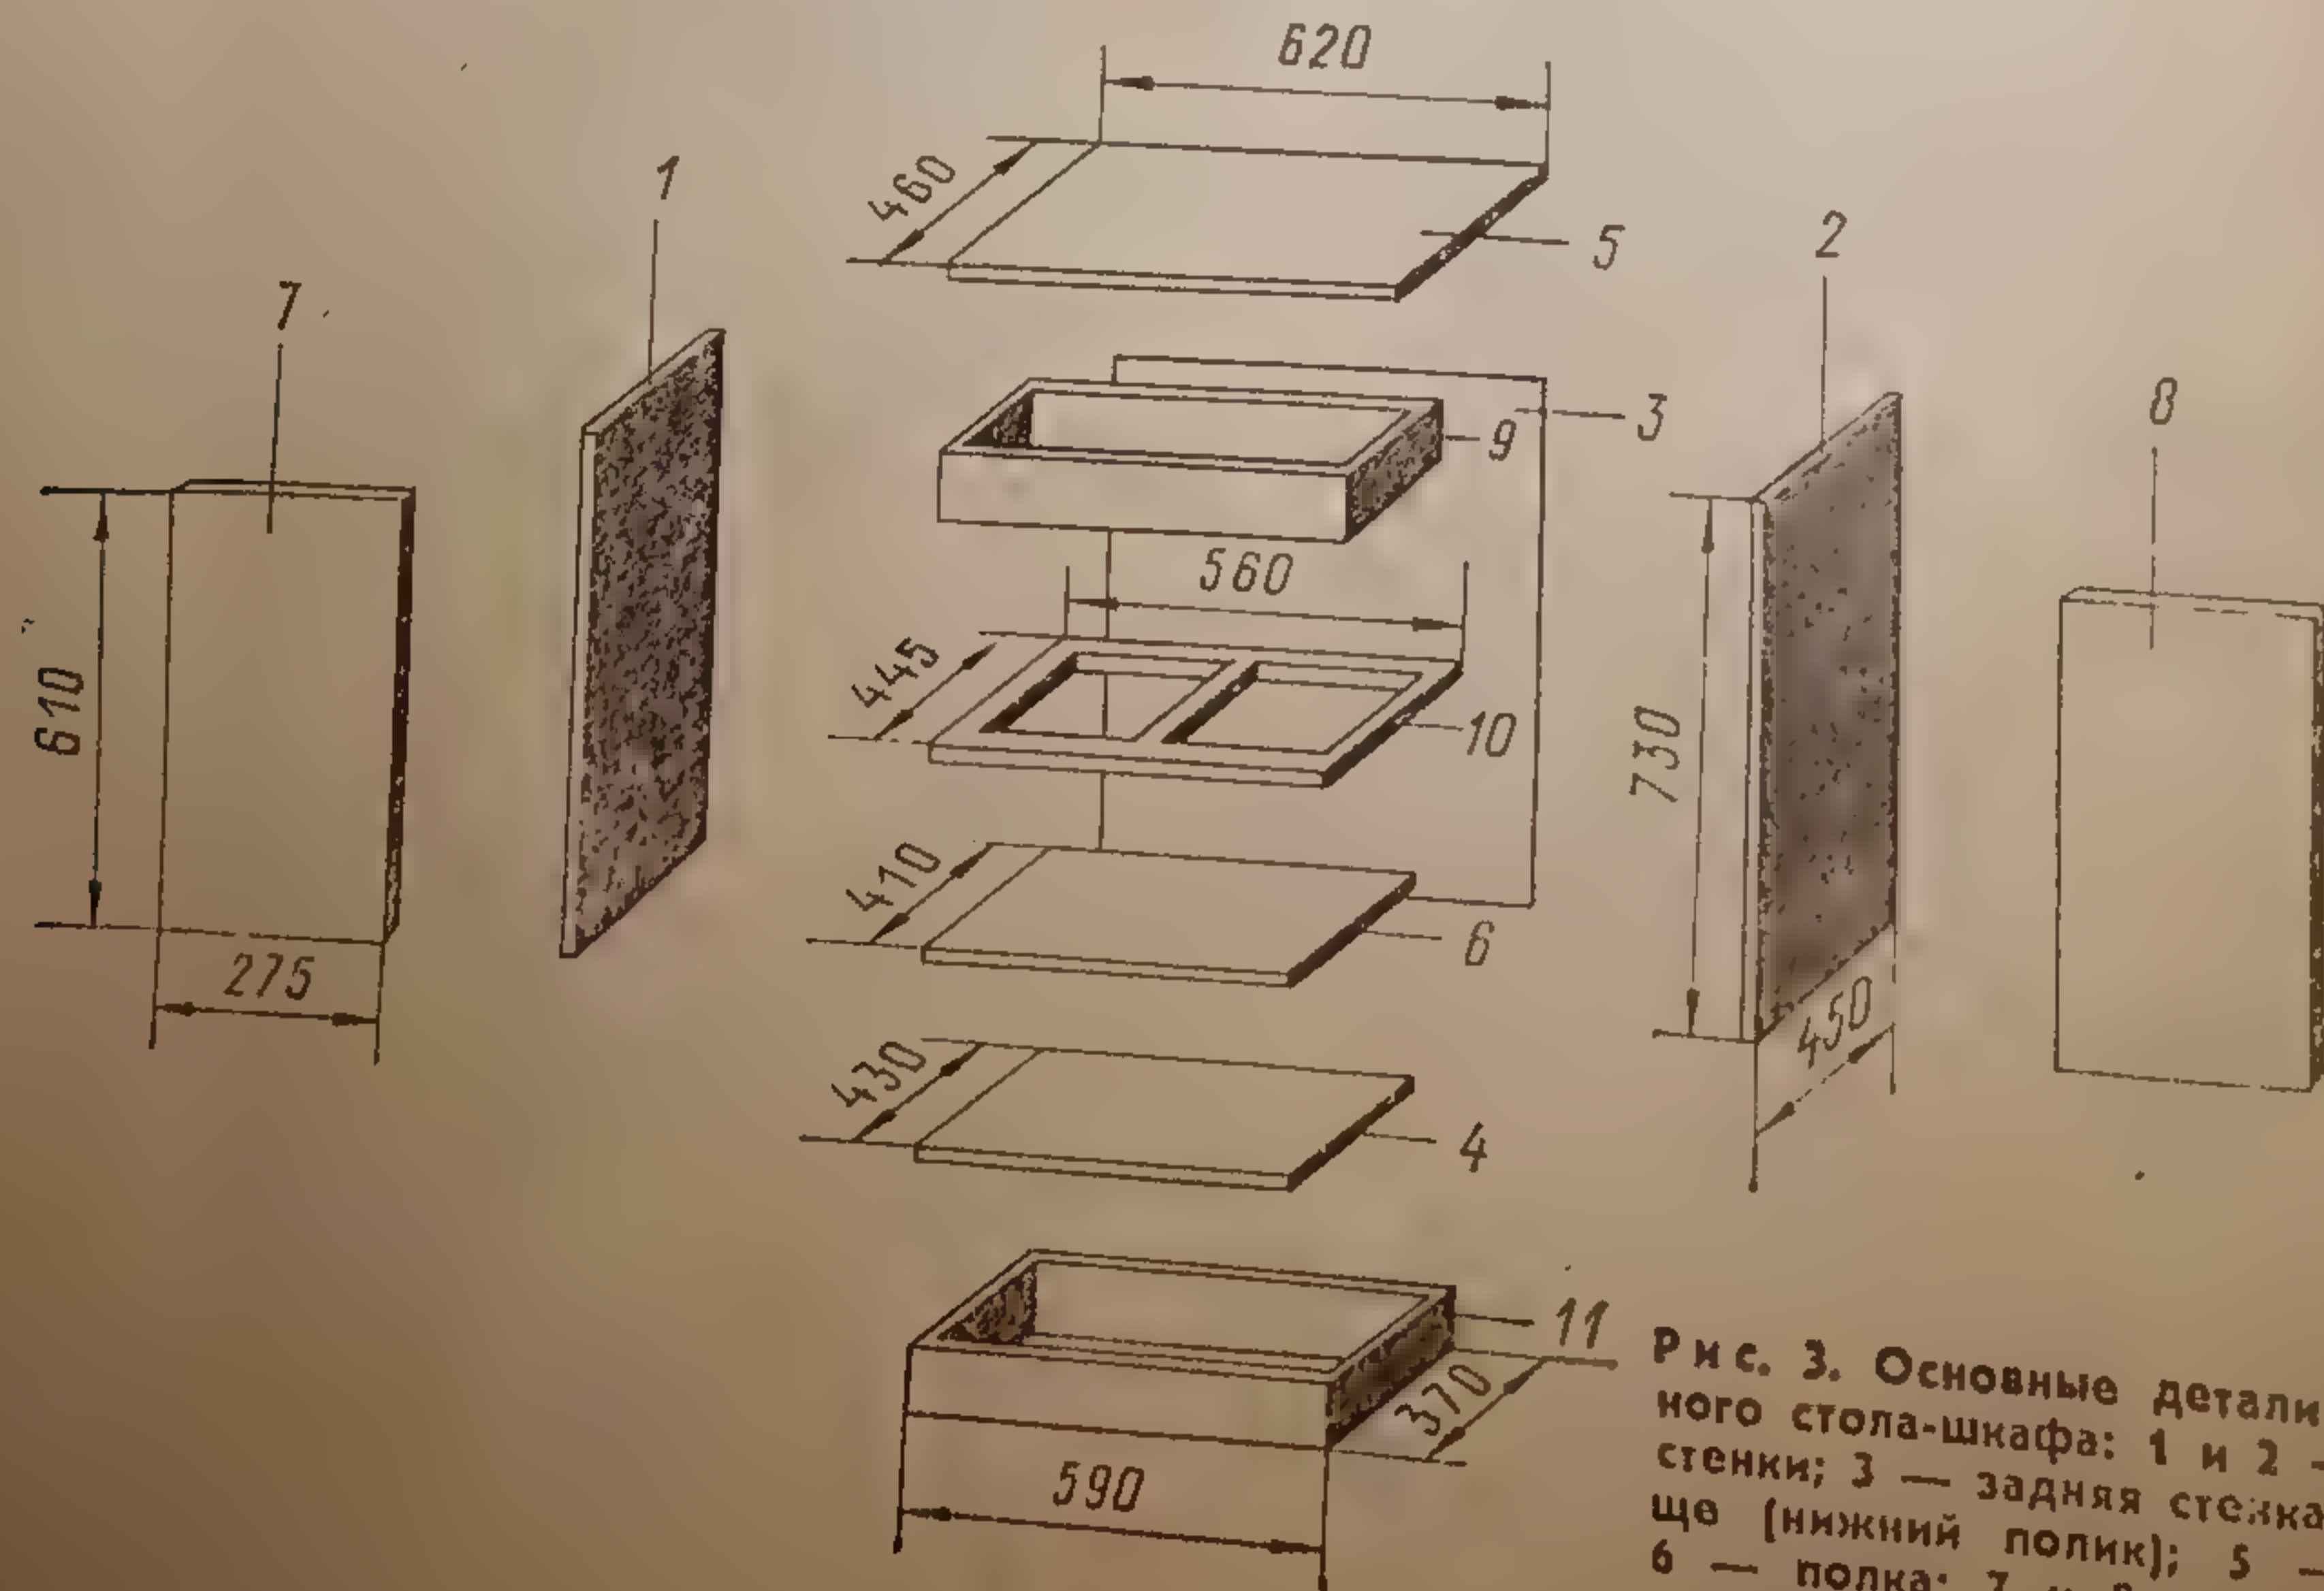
Основные детали разделочного стола-шкафа: 1 и 2 — боковые стенки; 3 — задняя стенка; 4 — днище (нижний полк); 5 — крышка; 6 — полка; 7 и 8 — дверки; 9 — ящик; 10 — подыщичная рамка; 11 — цоколь
